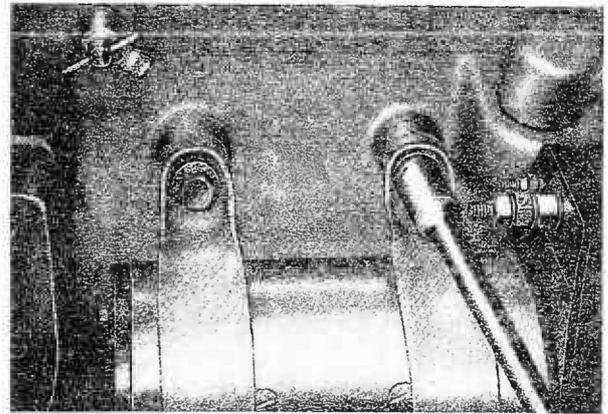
Befestigungsschrauben für Anlasser mit Steckschlüssel lösen
